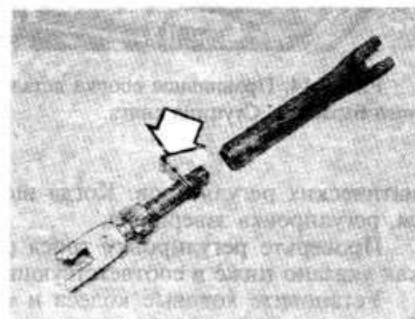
Детали регулировочного устройства колодки правого тормоза — термозажим указан стрелкой
